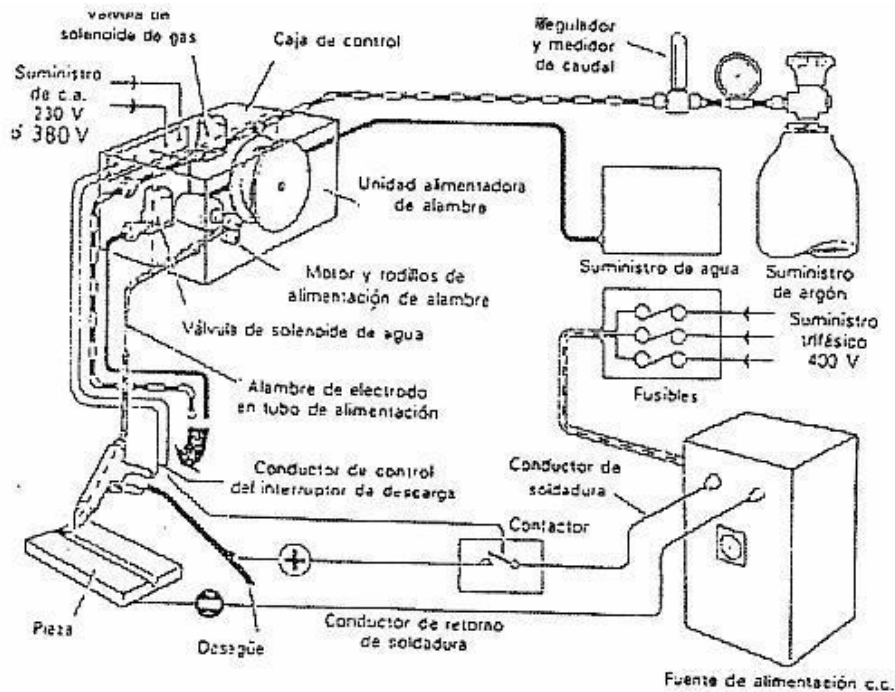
Máquina de soldadura MIG/MAG
